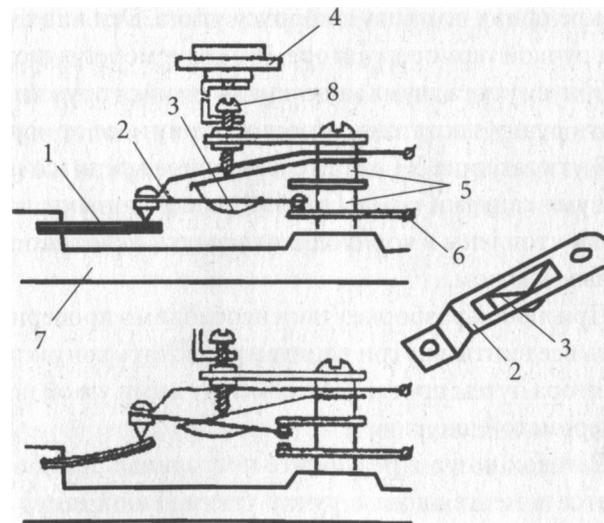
Терморегулятор утюга: 1 — биметаллическая пластина; 2 — подвижная контактная пластина; 3 — пружина подвижного контакта; 4 — ручка терморегулятора; 5 — изолирующие шайбы; 6 — пластина неподвижного контакта; 7 — подошва утюга; 8 — регулировочный винт
